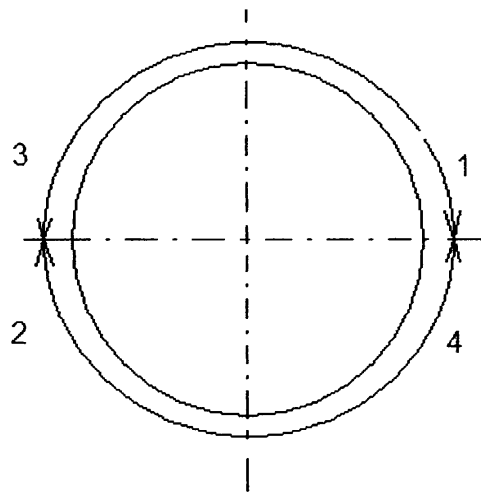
Схема сварки в 4 шва навстречу друг другу
